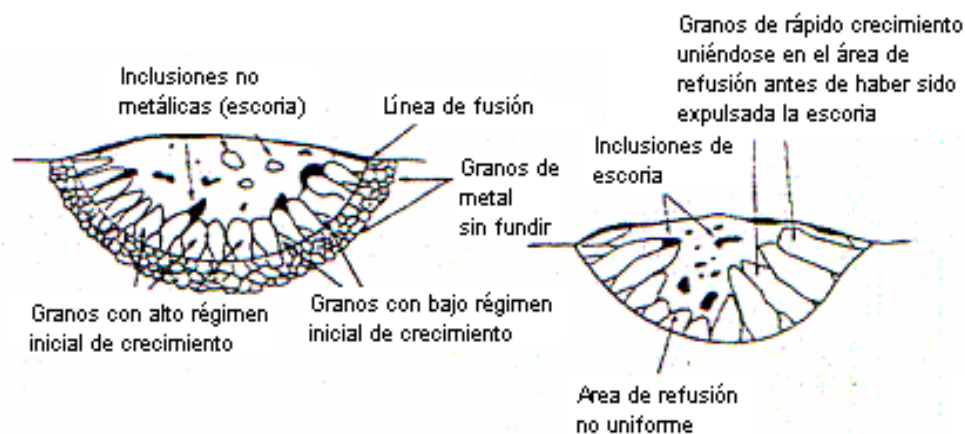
Sección transversal de cordones de soldadura en los que se aprecian inclusiones de escoria.
